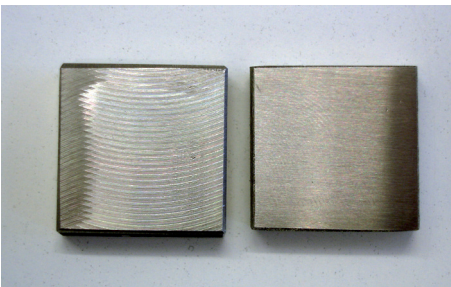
Oberfläche der Druckscherprüfkörper in gedrehter (links) und geschliffenen (rechts) Ausführung.
